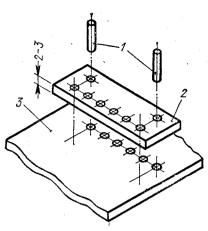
Приспособление для сверления рядов круглых отверстий: 1 — штифты: 2 — кондуктор; 3 — панель.
